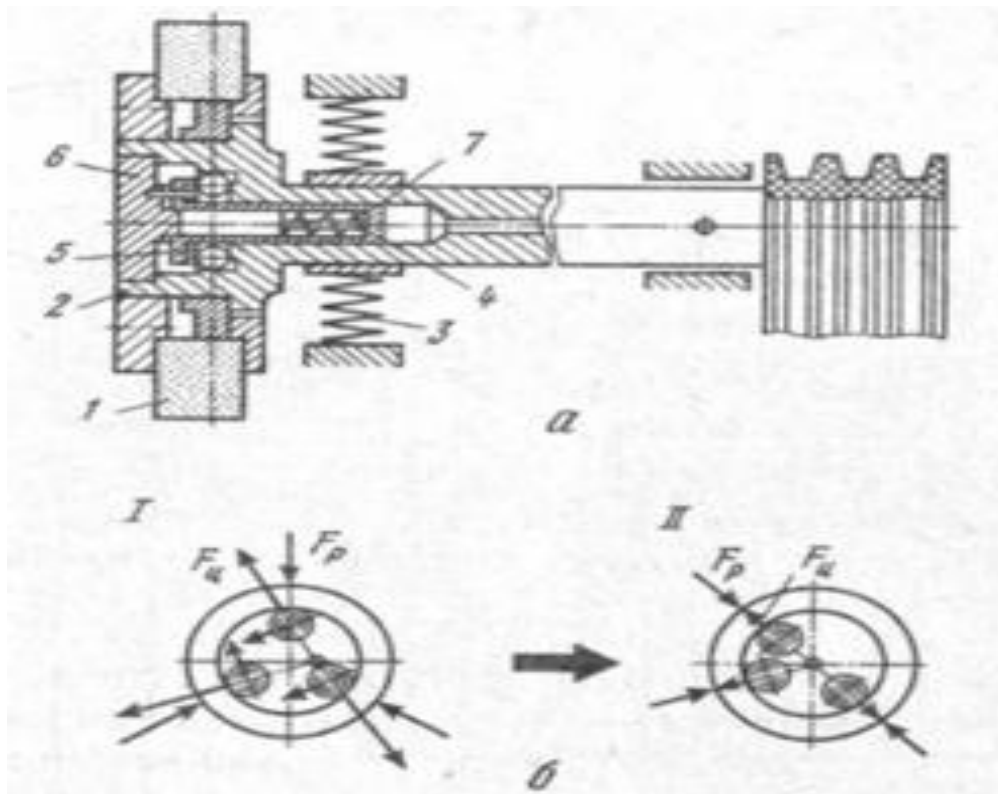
Схема автоматического устройства для балансировки кругов с шаровыми массами: а – конструкция, б – положение шаров и центра масс до и после балансировки, 1 – круг, 2 – шпиндель, 3 – пружинные опоры, 4 – шток гидроцилиндра, 5 – грибок зажимной, 6 – крышка, 7 – пружина.
